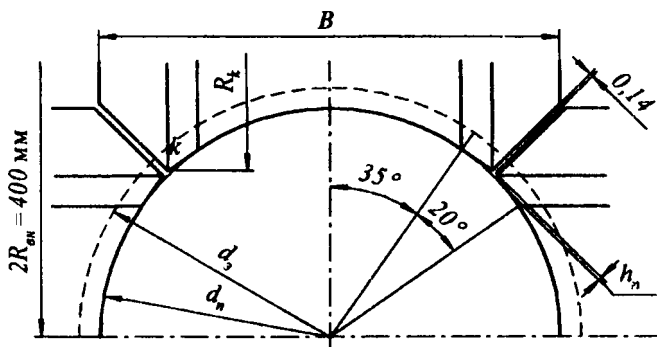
Схема калибровки «круг-круг» с подрезанием фасок
